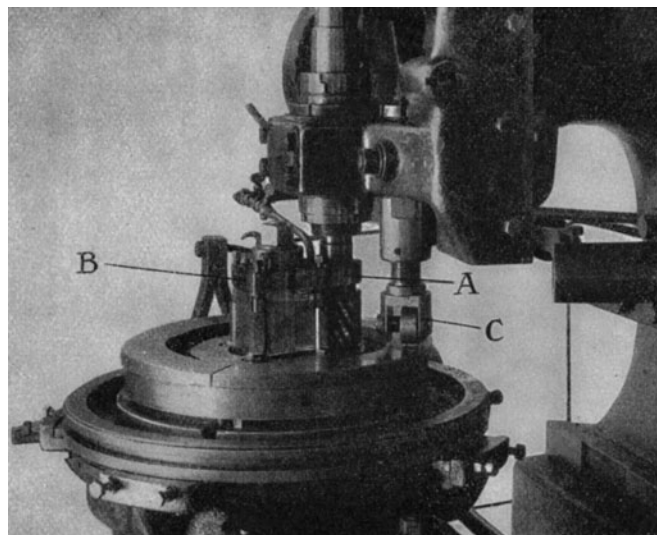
Fräsen des Schaufelrückens und des schrägen Fußansatzes.
